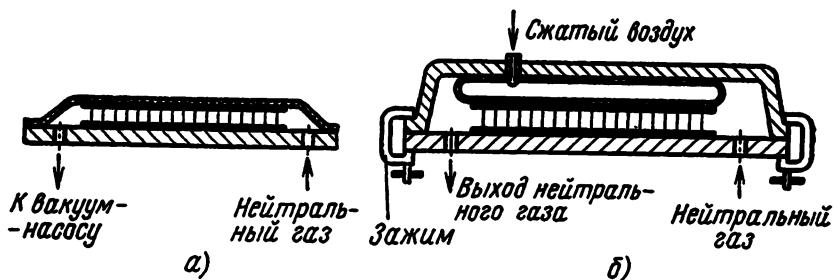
Приспособление для пайки сотовых конструкций с вакуумным (а) и пневматическим (б) прижимом
